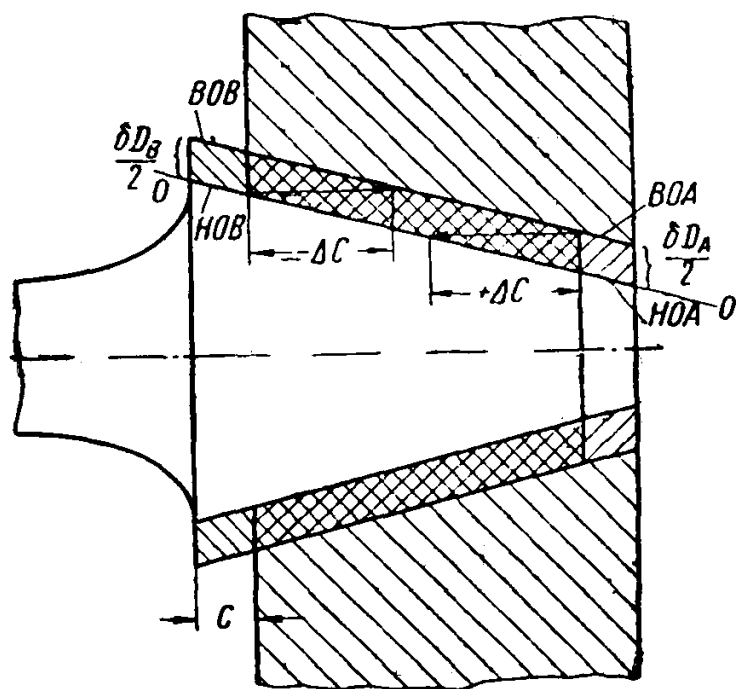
Схема полей допусков на диаметры конусных деталей
